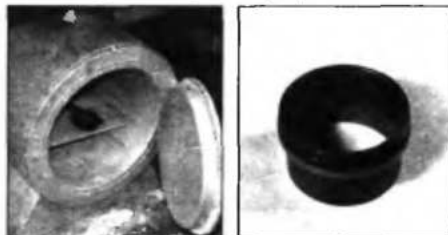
Электропечь для нагрева деталей перед сборкой
